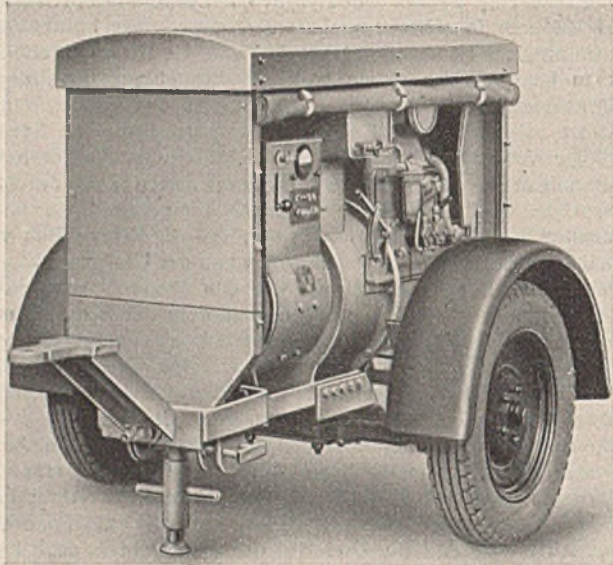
Schweißumformer von Messer & Co. G. m. b. H. für eine Nennleistung bis 250 A mit Antrieb durch einen Dieselmotor.
